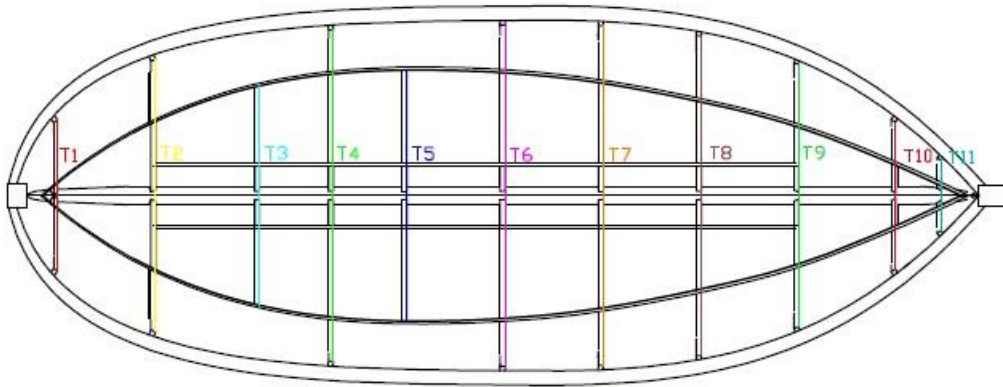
Refuerzos transversales (Fuente: elaboración propia)
